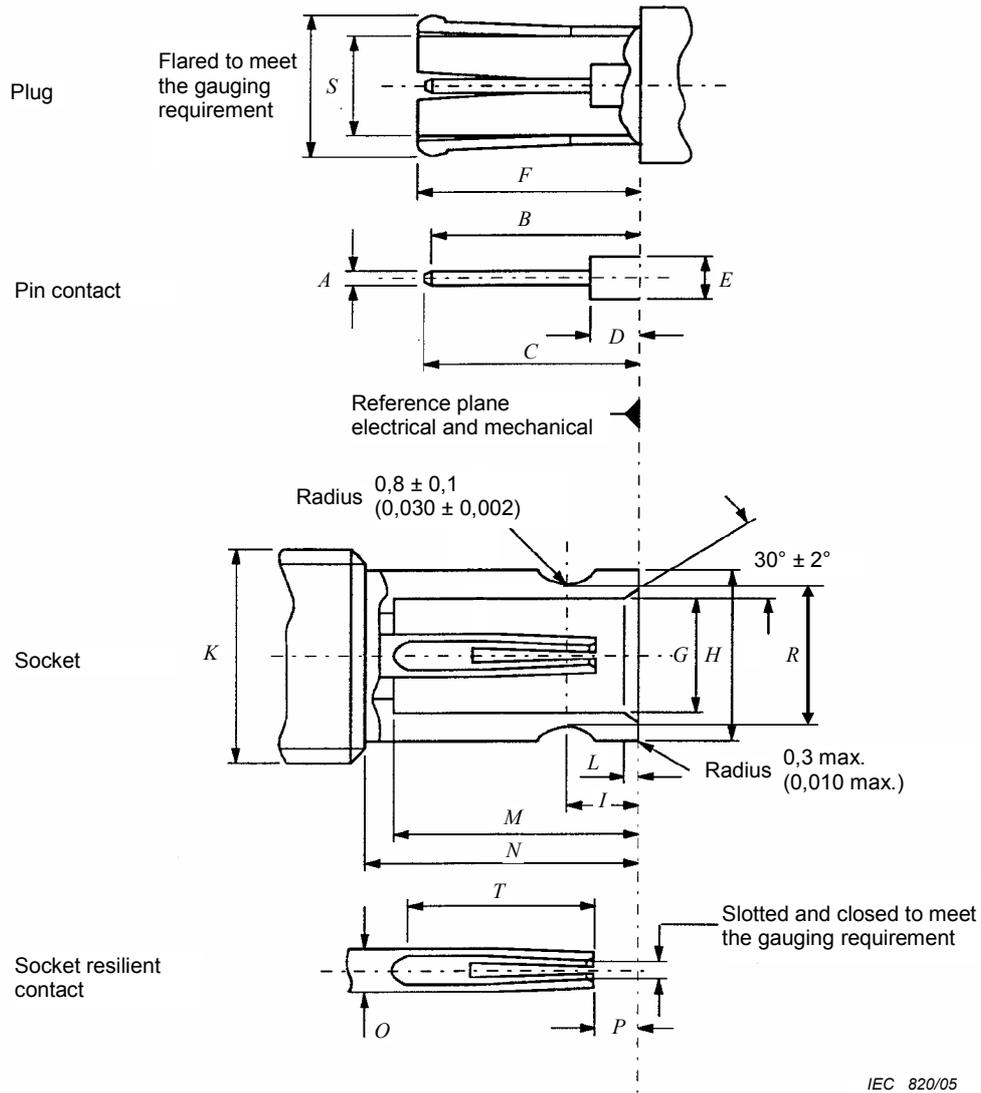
Interfaces (pour les dimensions, voir Tableau 1)
